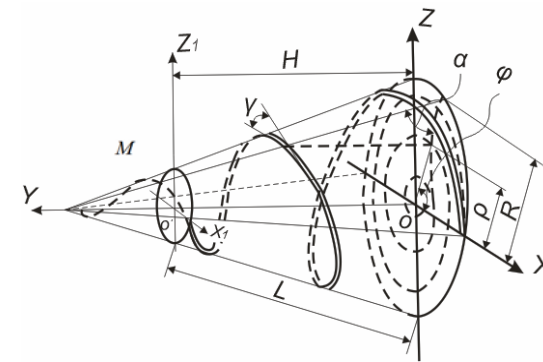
Схема для визначення довжини прутка, з якого виготовляється конічний валець
